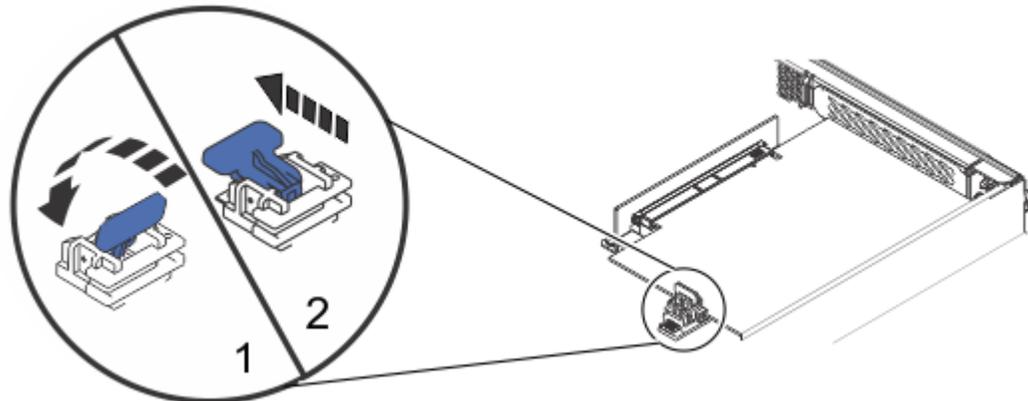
Sicherungsriegel des PCIe-Adapters entfernen
